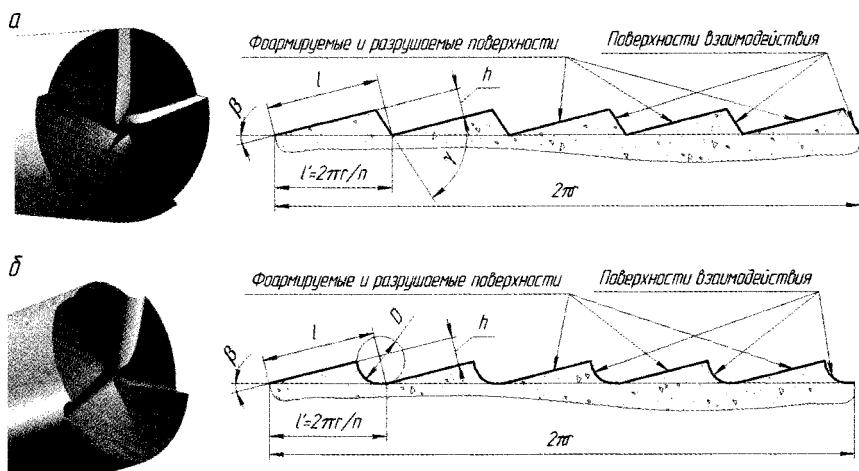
Развертка цилиндрического сечения поверхности забоя с линейным профилем ПВ (а) и с цилиндрической ПВ (б)
